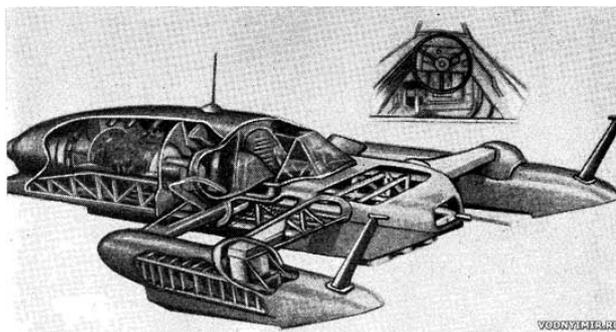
Типовой трехточечный глиссер с кормовым расположением двигателей
